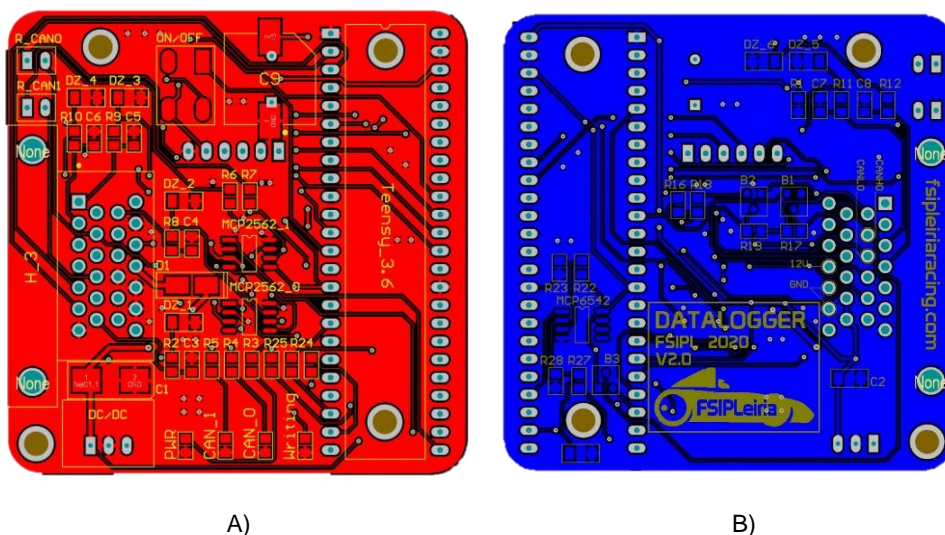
Design Final da PCB do Datalogger - 2D. A) Top Layer, B) Bottom Layer.
